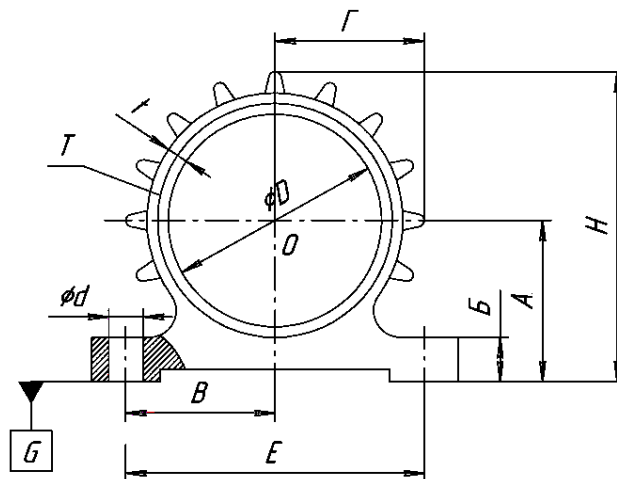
Эскиз заготовки типа корпуса электродвигателя
